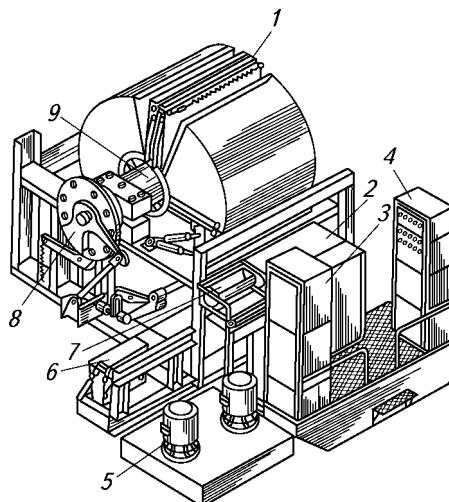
Роторный скроморозильный агрегат MAP-8AM:
